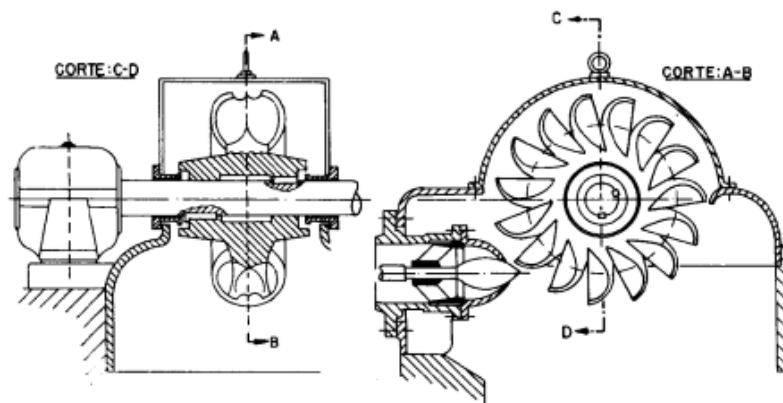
Desenho técnico da arquitetura de instalação de uma Turbina Pelton
